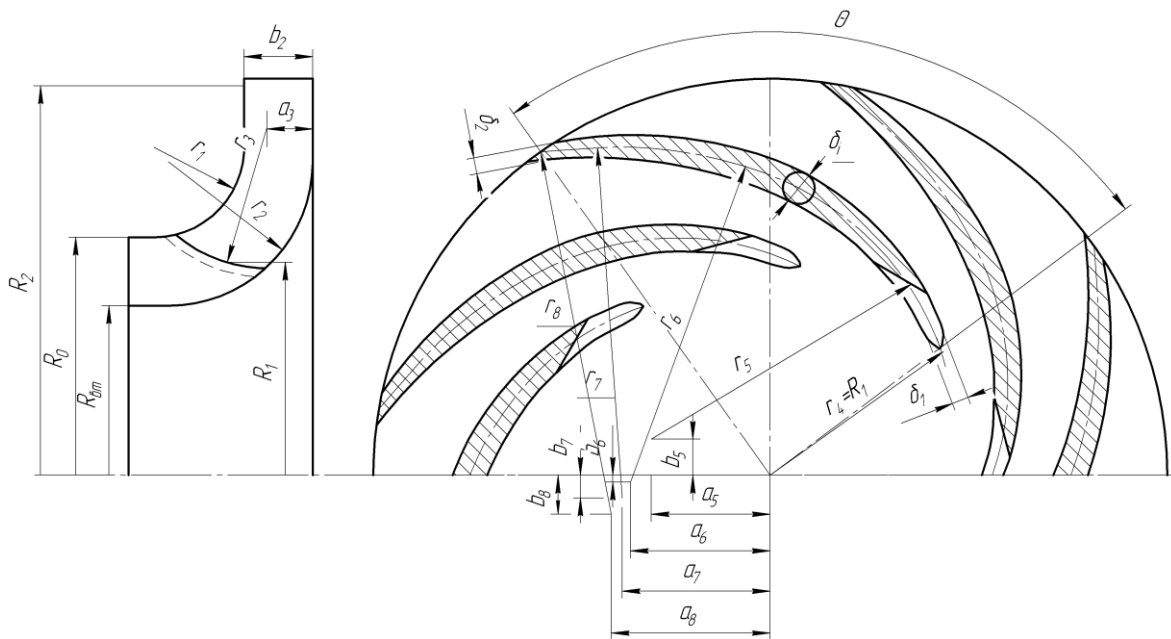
Побудова циліндрової лопаті робочого колеса
